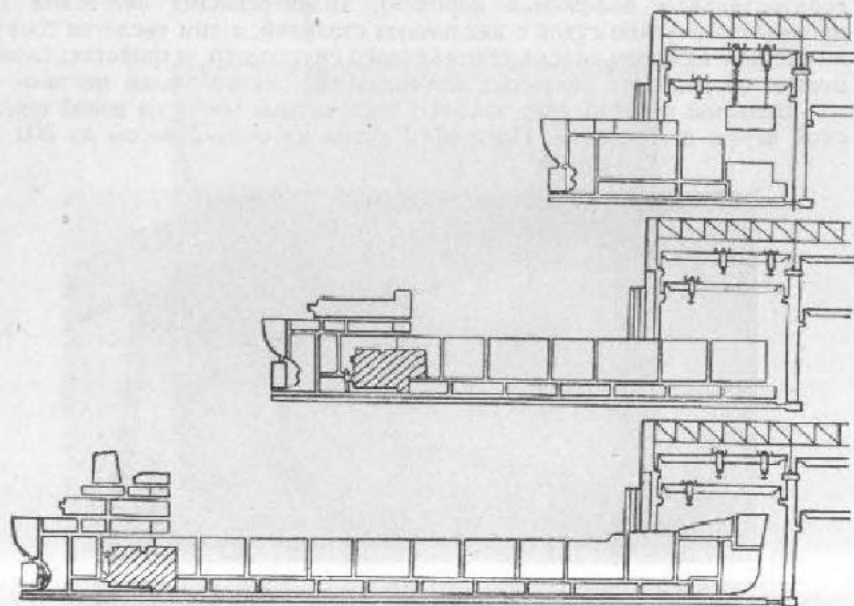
Сборка корпуса на верфи в Арендале (Швеция).
